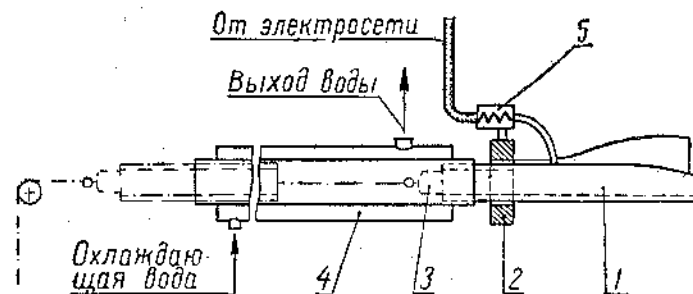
Приспособление для изготовления сварных труб из термопластов.
